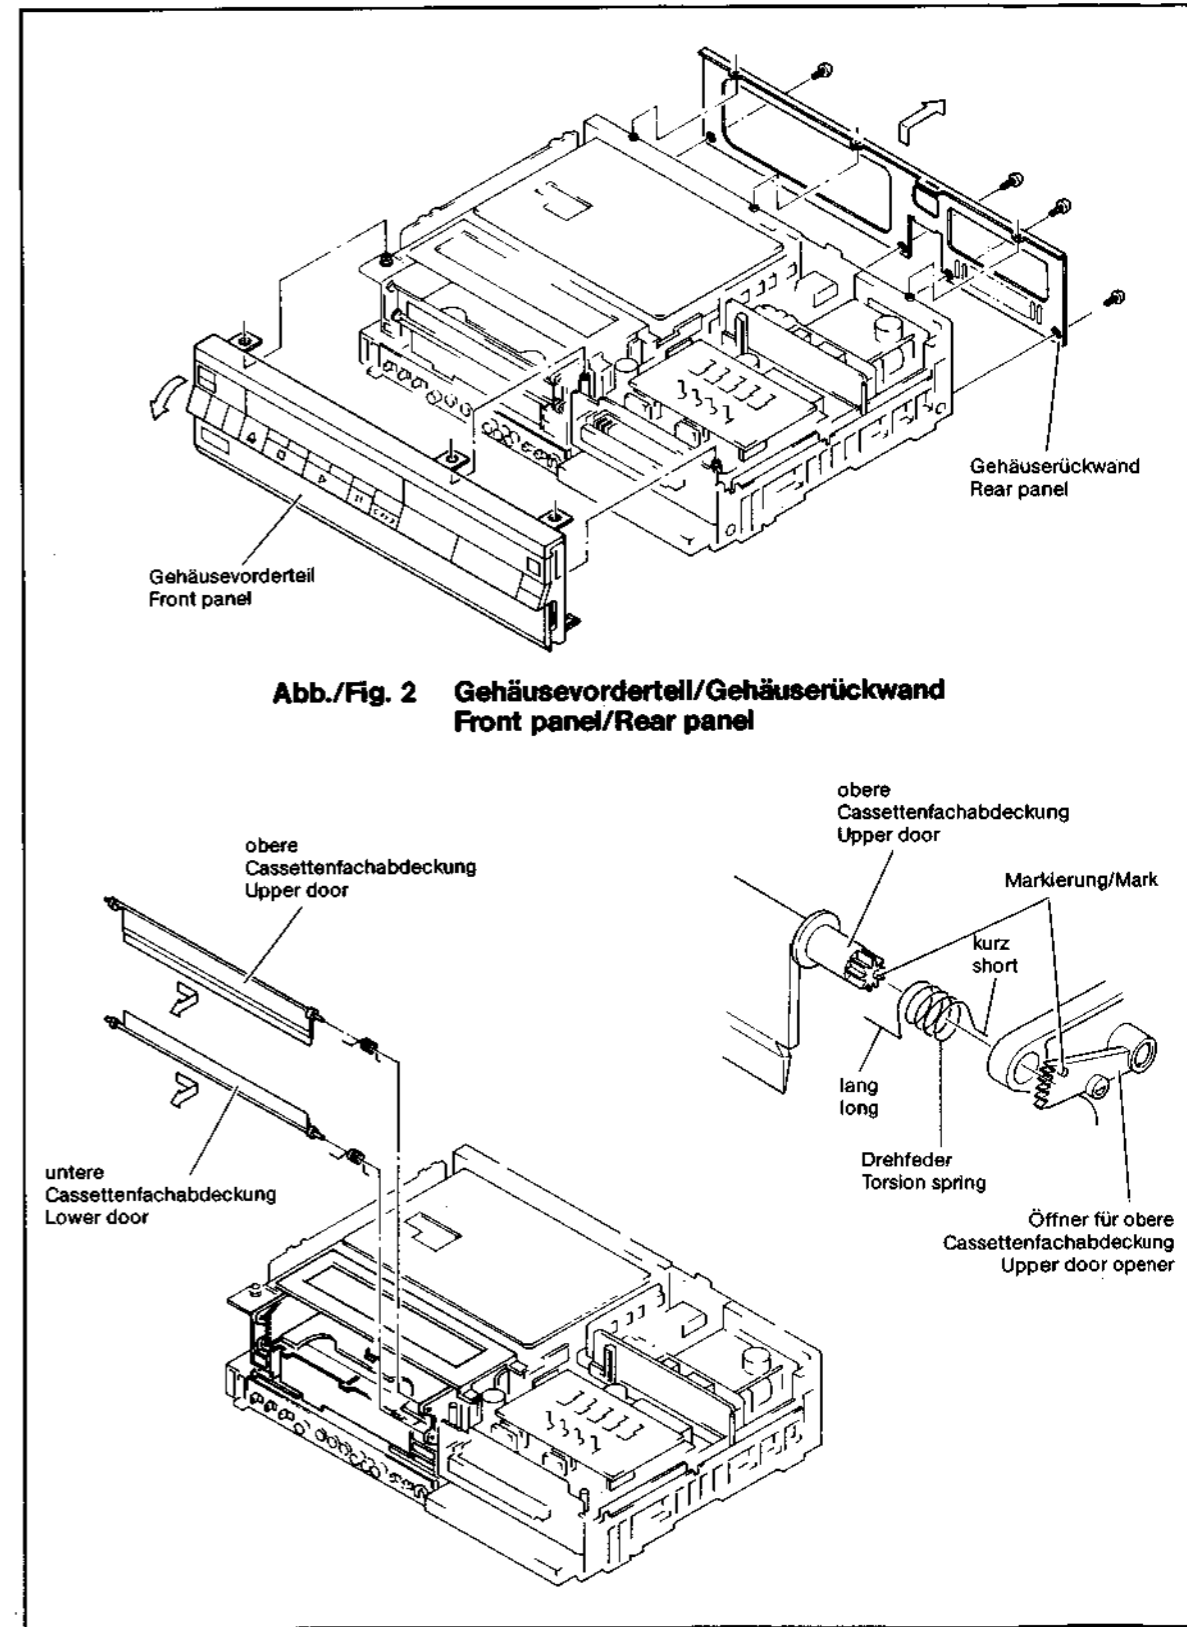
Gehäusevorderteil/Gehäuserückwand
